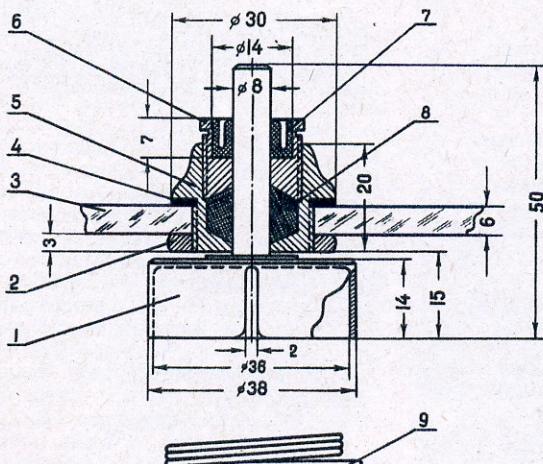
Механизм перемотки пленки: 1 — барабан; 2 — гайка; 3 — крышка бокса; 4 — резиновая прокладка; 5 — корпус сальника; 6 — уплотнительная гайка; 7 — самоуплотняющаяся манжета; 8 — сальник; 9 — пружина
